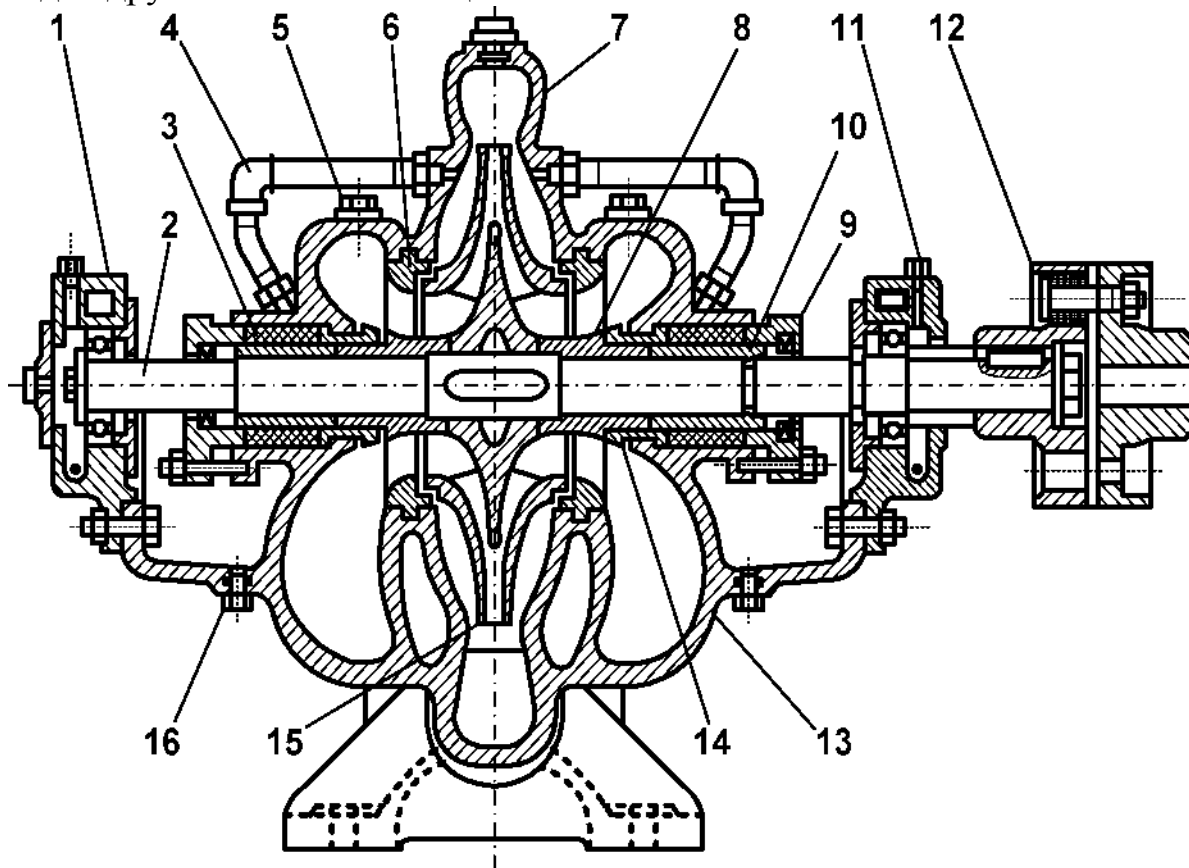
Насос Д200-95: 1 и 11 - радиальные подшипники; 2 - вал; 3 - сальниковое уплотнение; 4 - переводная трубка; 5 - пробка; 6 - уплотняющие кольца; 8 и 14 - направляющие и защитные втулки; 7 - крышка корпуса; 9 - фланец сальника; 10 - защитная втулка; 12 - упругая муфта; 13 - корпус; 15 - рабочее колесо двустороннего входа; 16 - отвод дренажа
